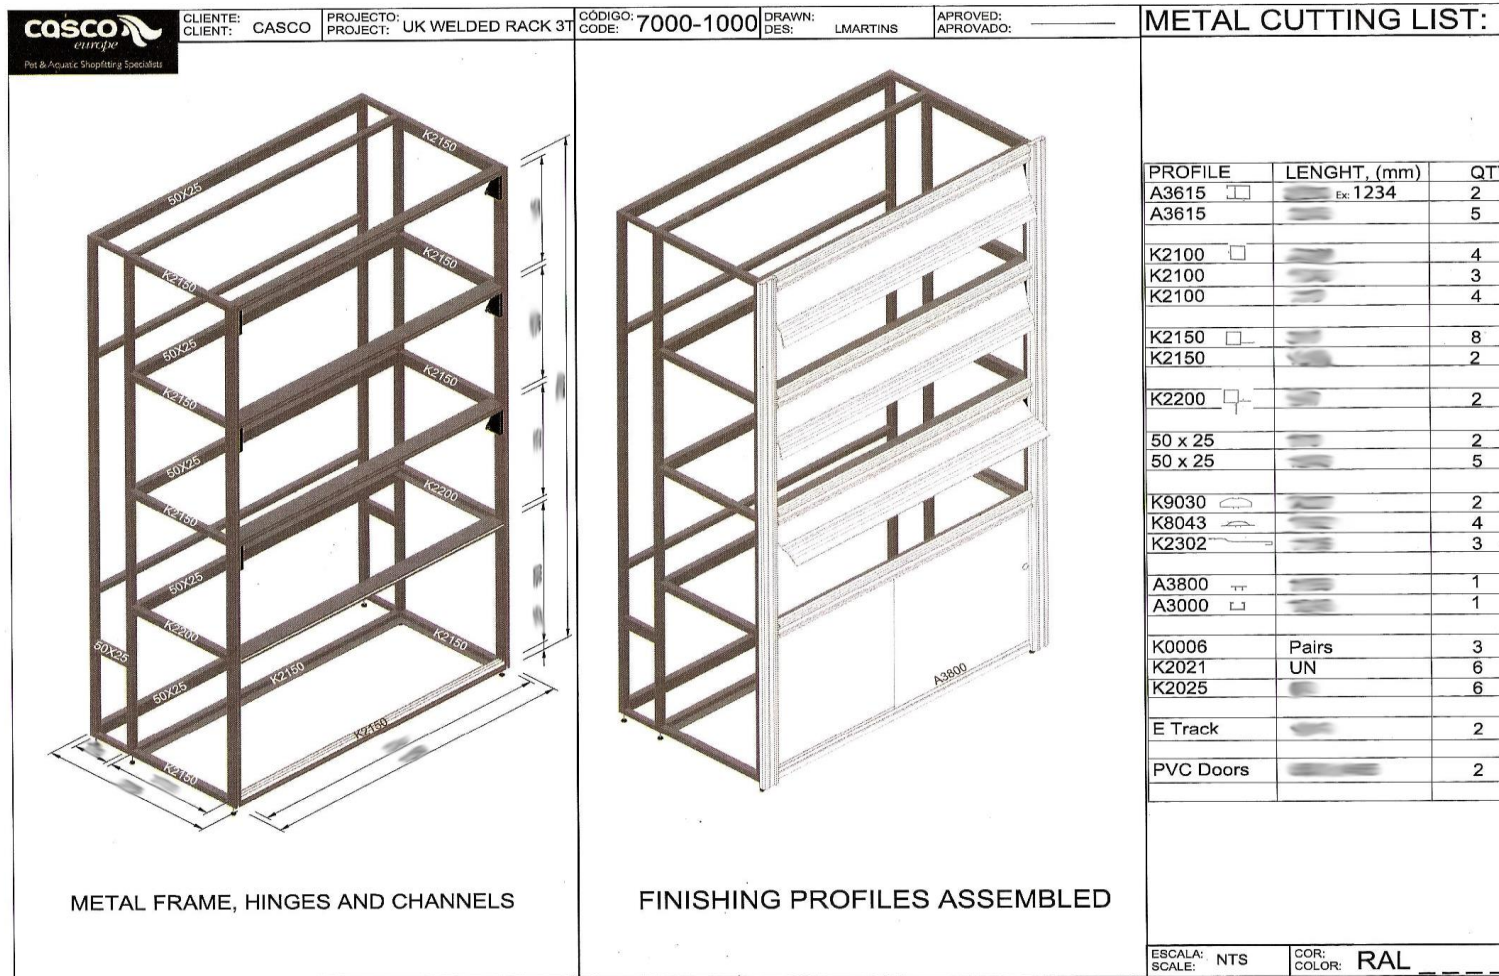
Desenho técnico detalhado onde o colaborador do posto de corte só necessita de executar a tarefa de corte. ¹
